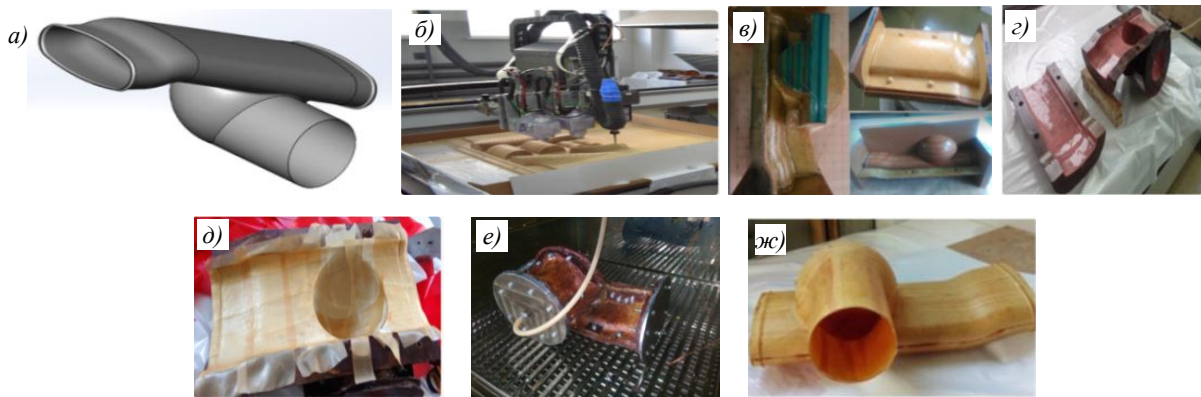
Технологический процесс изготовления формообразующей оснастки и заготовки системы кондиционирования воздуха (СКВ) из ПКМ: а – математическая модель детали; б – изготовление мастер-модели; в – выкладка оснастки; г – формообразующая оснастка из стеклопластика; д – выкладка детали; е – формование детали; ж – готовая заготовка СКВ из ПКМ
